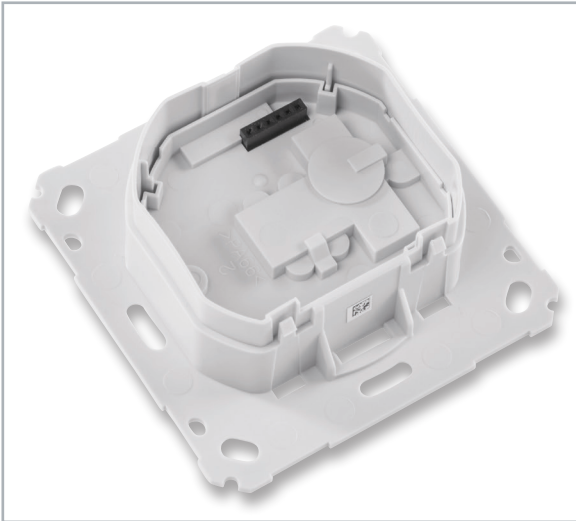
Die Lage der Isolierplatte ist durch die vorhandene Öffnung vorgegeben, Führungen sichern eine stabile Lage.
